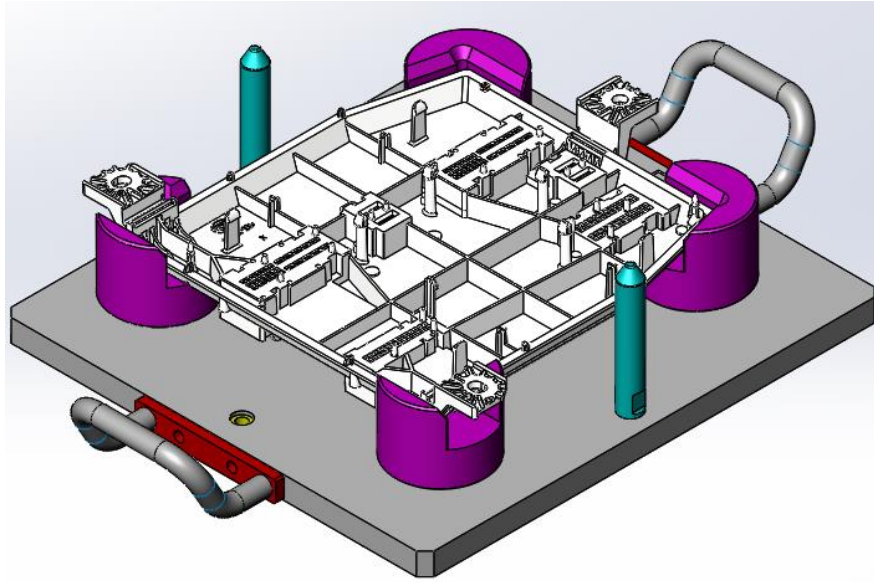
Ensamble de pallet (alojamientos con tapa superior)
